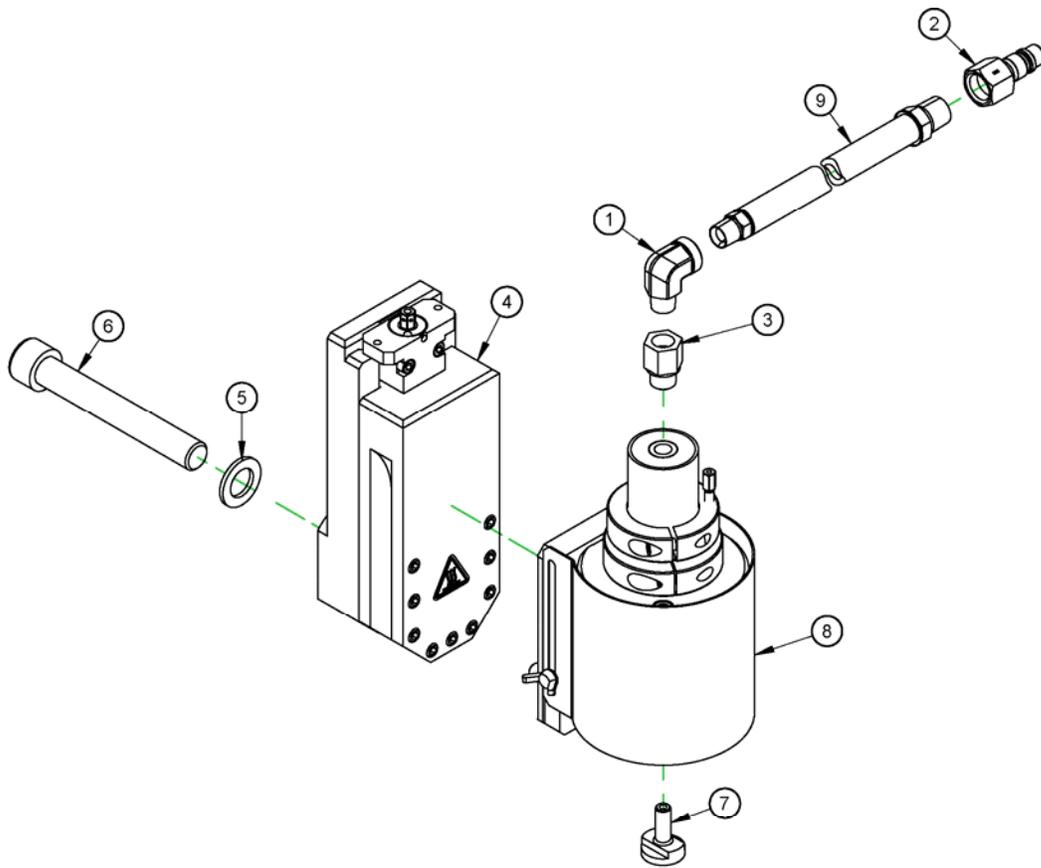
ENSEMBLE DE BRAS D'USINAGE (P/N 57872)
